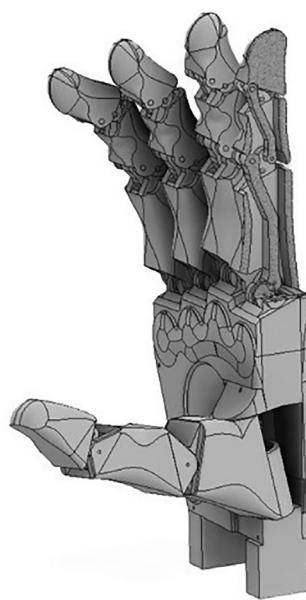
3D-модель предлагаемой конструкции протеза руки
